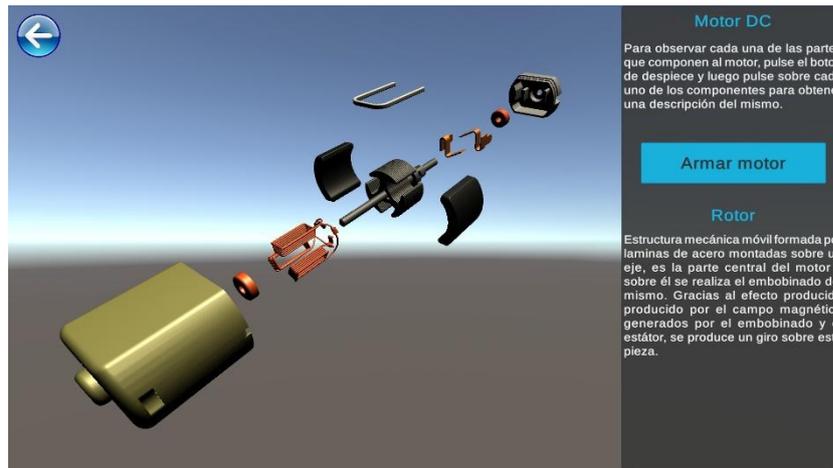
Aspecto escena Motor con despiece del motor y descripción de la pieza rotor
